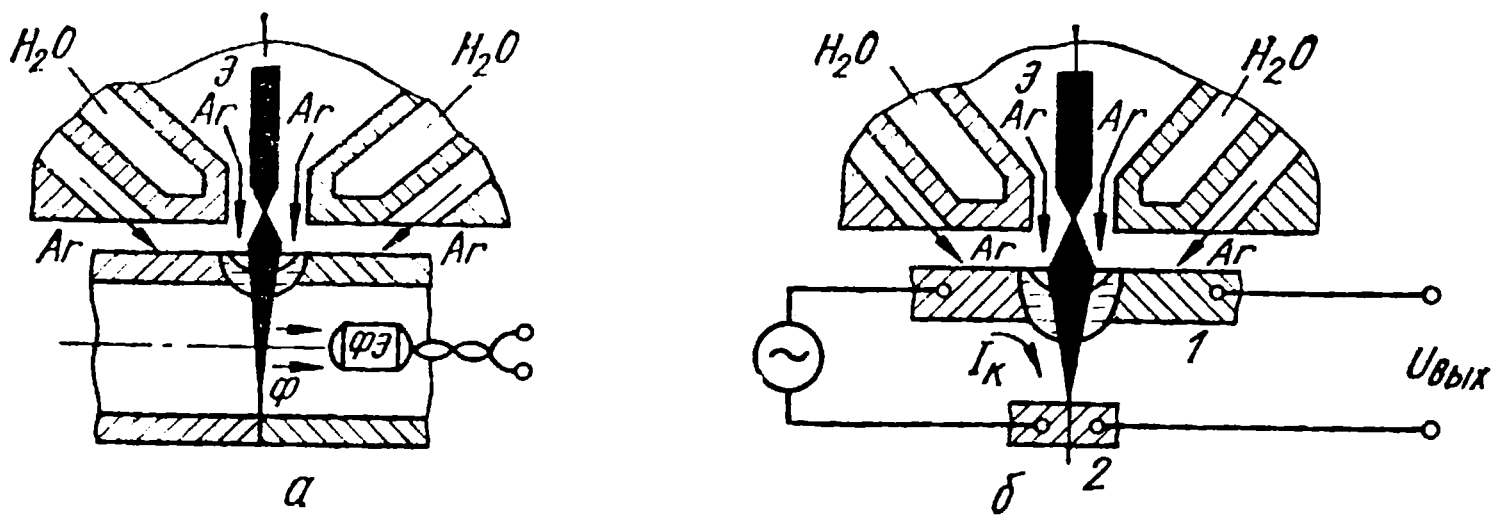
Способы контроля проплавления при плазменной сварке
